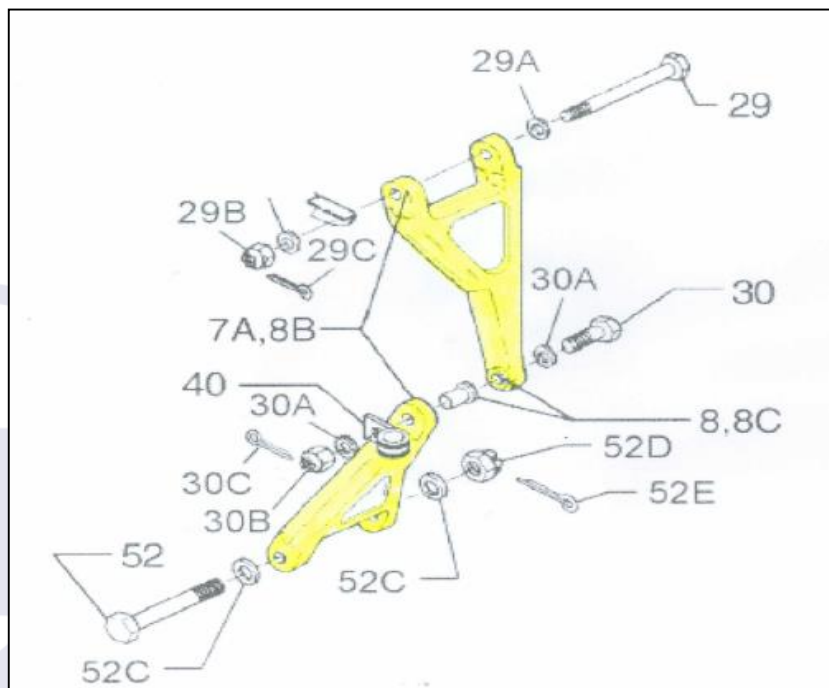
Detalhe dos componentes do *Link Assy - Landing Gear Torque*.
